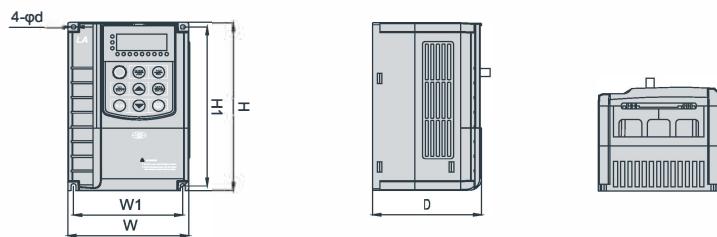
铁壳壁挂式:22-500kW Steel, wall type
